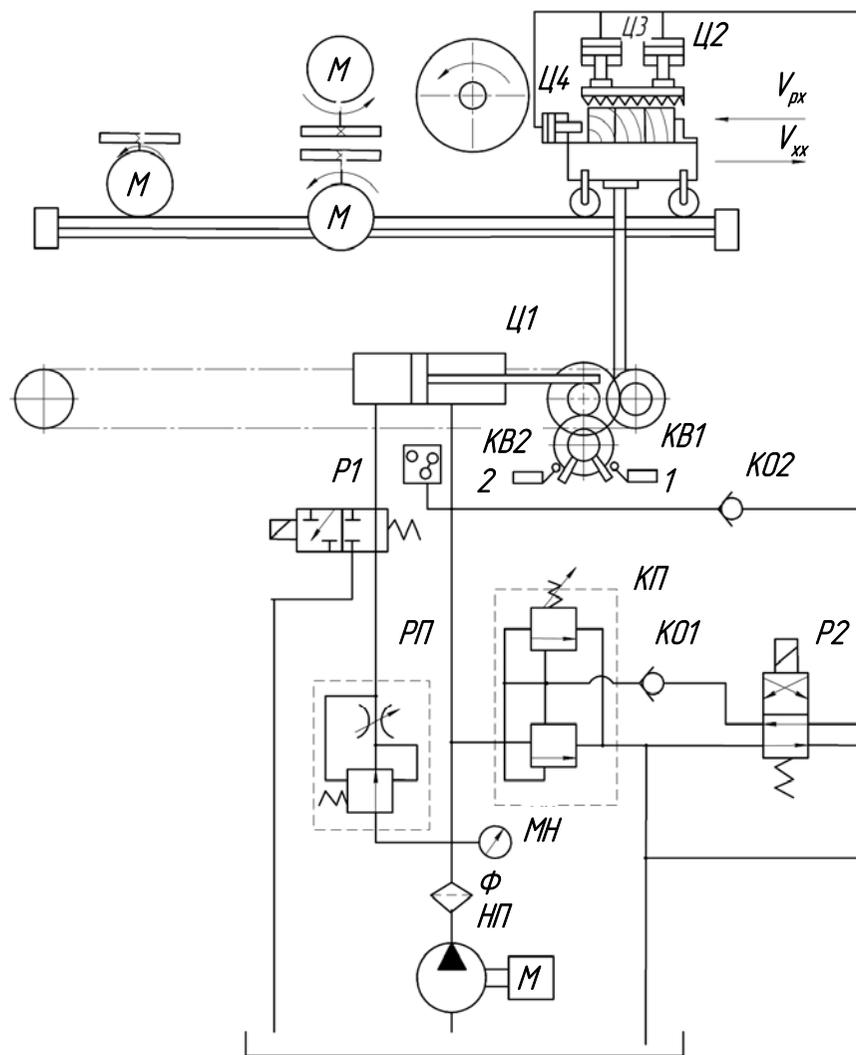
Гидрокинематическая схема шипорезного одностороннего станка ШО16-4
